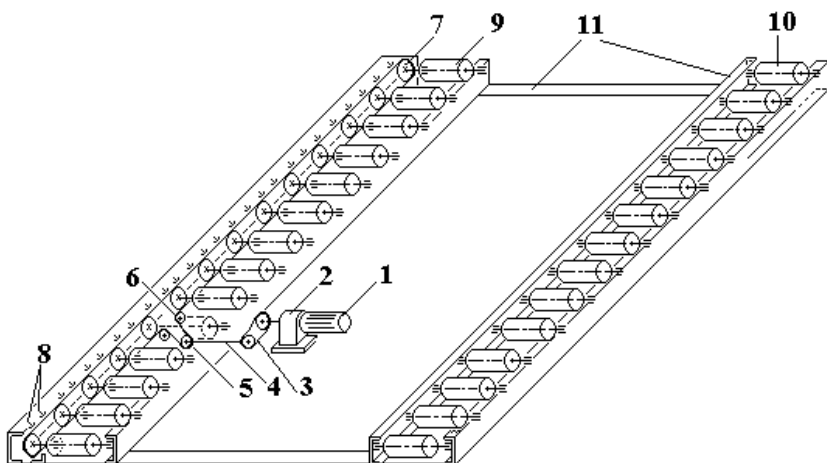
Схема устройства и привода сборочной секции транспортера: 1 – двигатель; 2 – планетарный редуктор; 3 – цепная передача; 4 – валик; 5 – главная тяговая звёздочка; 6 – натяжная звёздочка; 7 – приводная звёздочка; 8 – башмаки-натяжители цепи; 9 – ролик приводной; 10 – ролик неприводной стороны; 11 – рама
